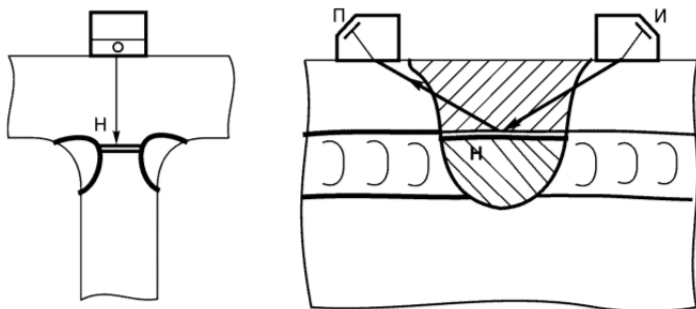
Схема прозвучивания таврового сварного соединения наклонными преобразователями по раздельной схеме (Н – непровар)
